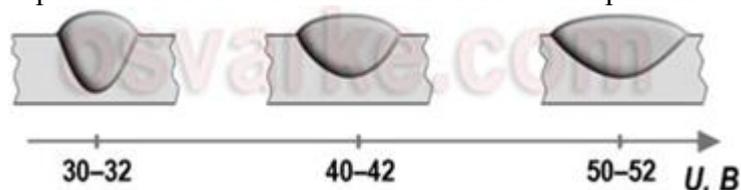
Влияние напряжения дуги на форму и размеры сварного шва
